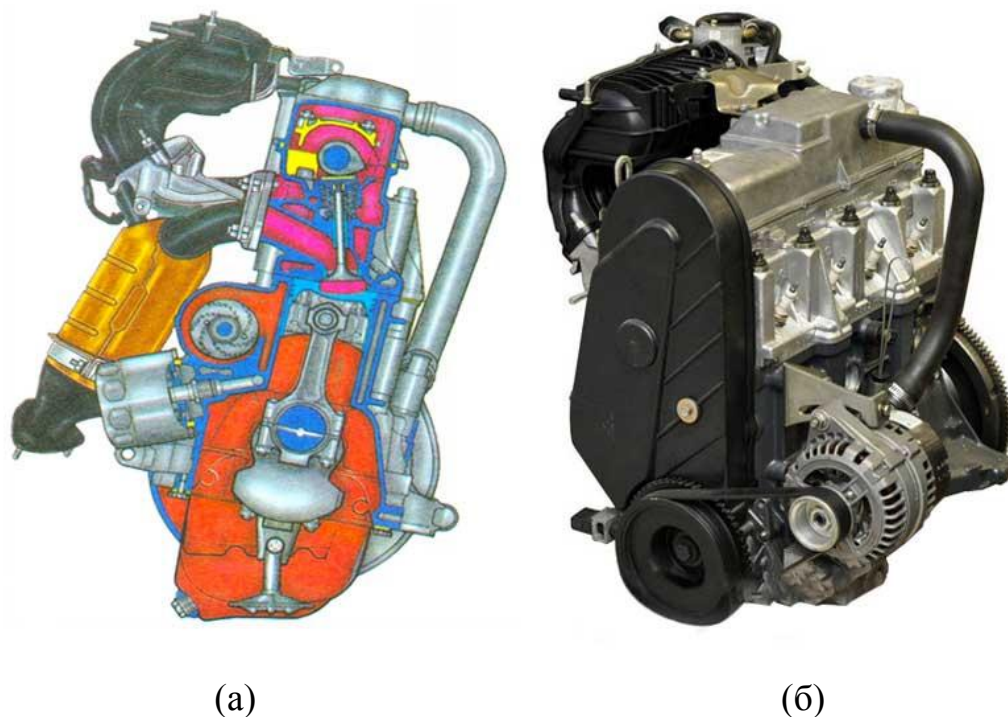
Устройство (а) и внешний вид (б) двигателя LADA Kalina
